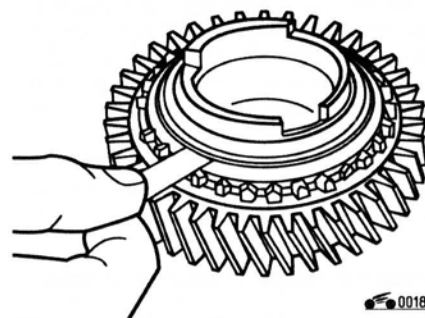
Проверка внутреннего кольца синхронизатора II передачи
